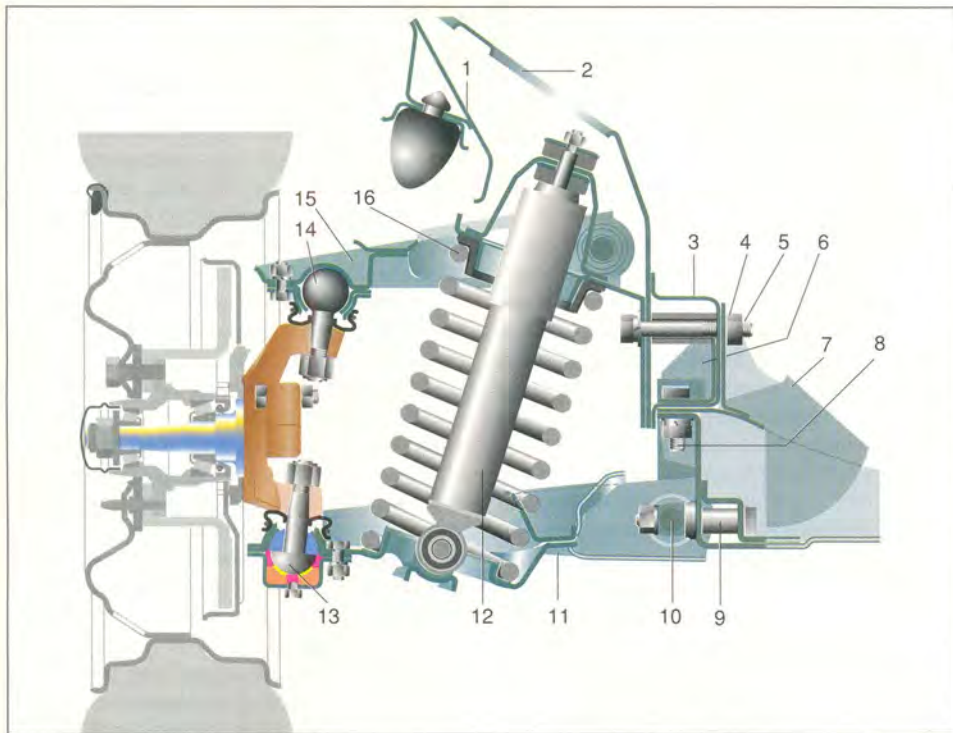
Схема передней подвески "Жигулей": 1 – стойка передка; 2 – брызговик; 3 – лонжерон; 4 – гайка; 5 – верхний горизонтальный болт; 6 – усилитель лонжерона; 7 – поперечина подвески; 8 – нижний вертикальный болт; 9 – болт крепления оси нижнего рычага; 10 – ось нижнего рычага; 11 – нижний рычаг; 12 – амортизатор; 13 – нижняя шаровая опора; 14 – верхняя шаровая опора; 15 – верхний рычаг; 16 – пружина.
